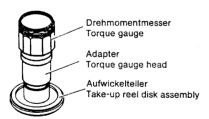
Aufwickelzug prüfen Fig. 3-5 Take up torque check
